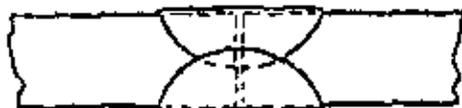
CORTE ESQUEMATICO DE UNA SOLDADURA DE "GRAN PENETRACION".
